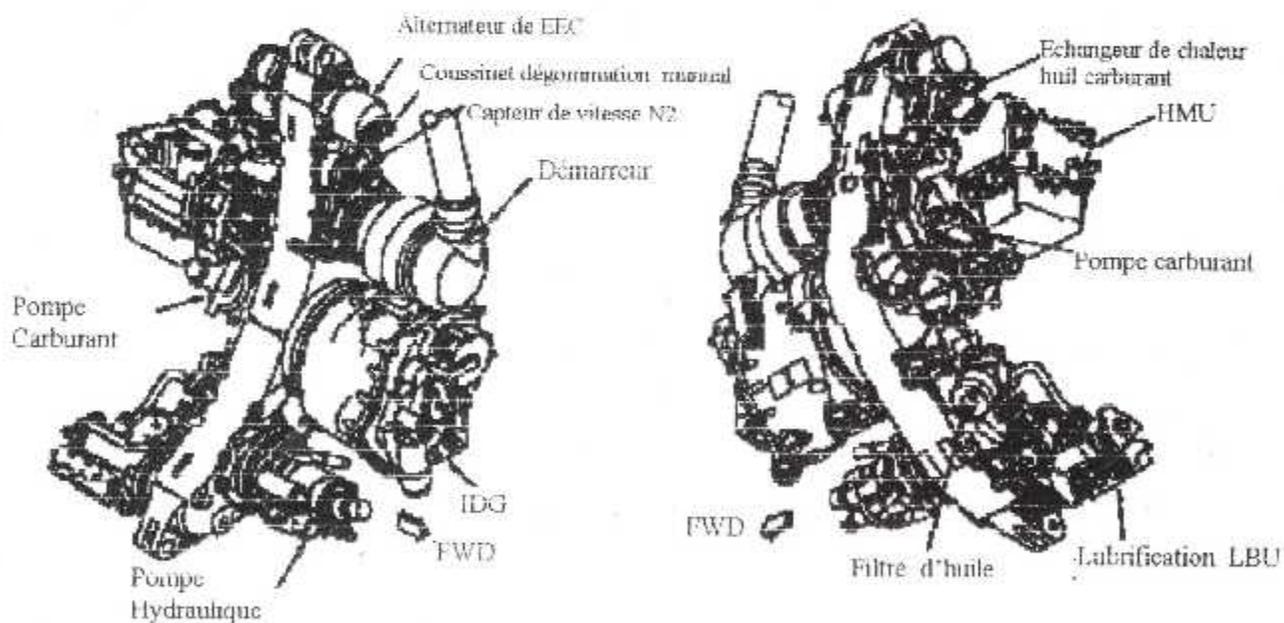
Les accessoires de la Gear Box (Module AGB)
